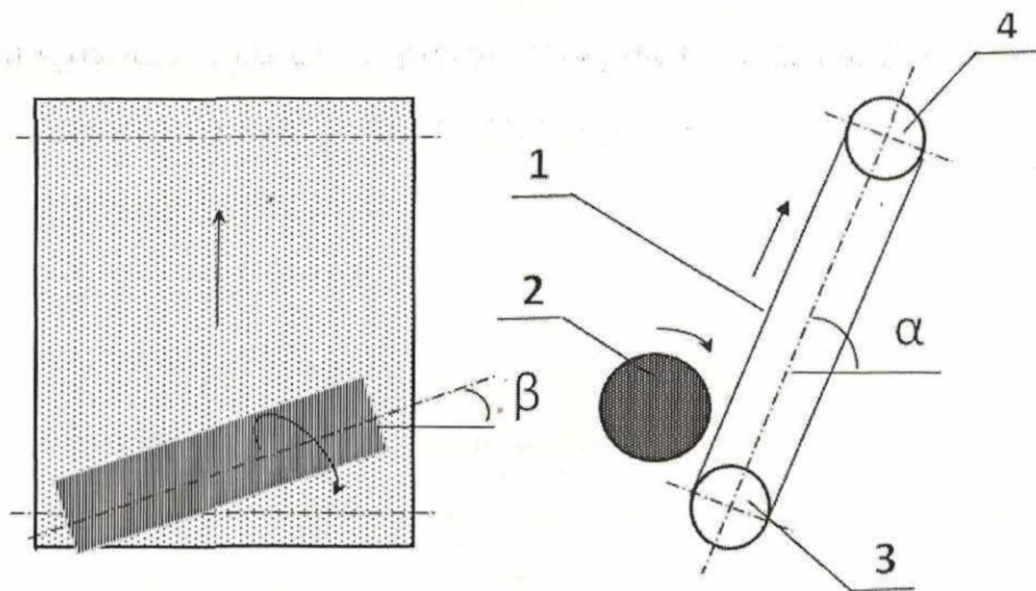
Схема удосконаленого очищувального робочого органу картоплезбирального комбайна: 1 - похила пальчаста гірка; 2 - валець з еластичною щіткою; 3 - нижній приводний барабан; 4 - верхній напрямний барабан
